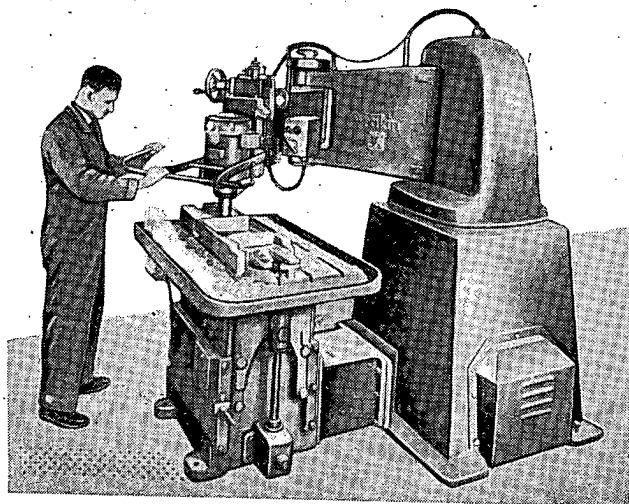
Радиально-фрезерный станок фирмы Вадкин мод. LYR. 1—постамент; 2—поворотная направляющая хобота; 3—хобот; 4—фрезерная головка; 5—рукоятка вертикального перемещения фрезерной головки; 6—суппорт; 7—высокочастотный преобразователь; 8—привод перемещения стола.
